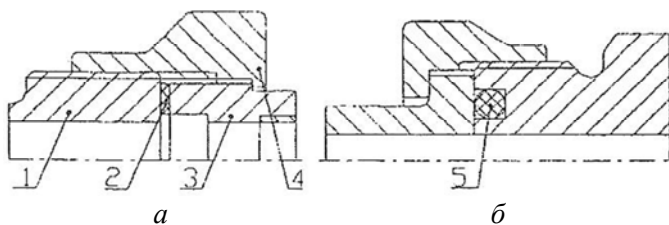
Схемы герметизации соединений трубопроводов:
